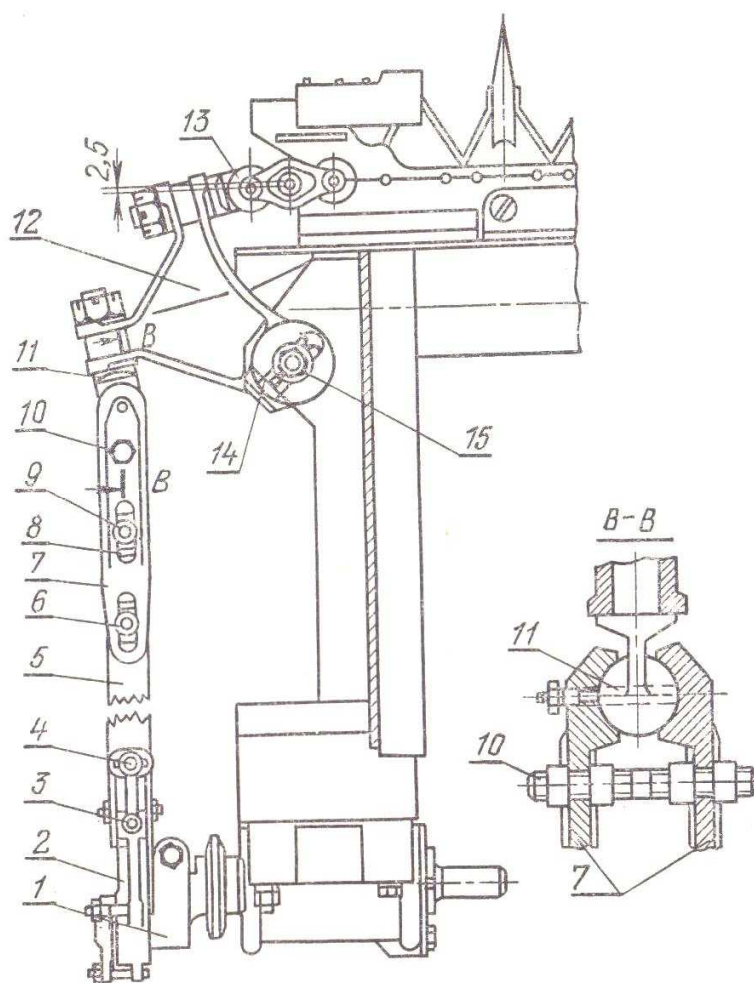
Привод ножа жатки комбайна СК-6: 1 – кривошип; 2 – головка; 3, 4, 6, 9, 15 – болты; 5 – шатун; 7 – щечки; 8 – зубчатая рейка; 10 – шпилька; 11 – шаровой болт; 12 – коромысло; 13 – щечки соединительного звена; 14 – конусные пазы
